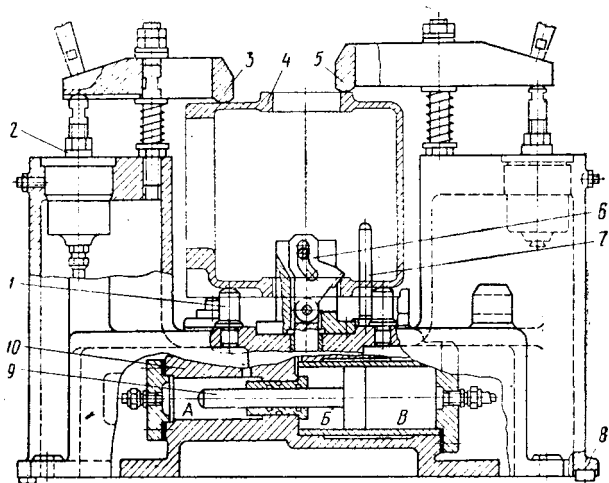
Приспособление с встроенным пневмогидравлическим усилителем для крепления корпусных деталей при фрезеровании
